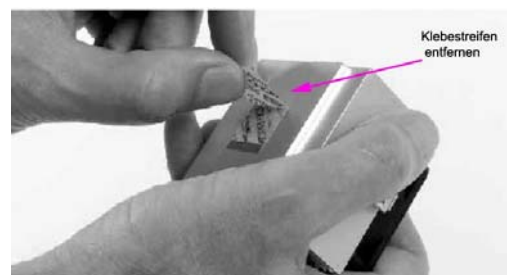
Entfernen des Klebestreifens vom Kühler [60]
